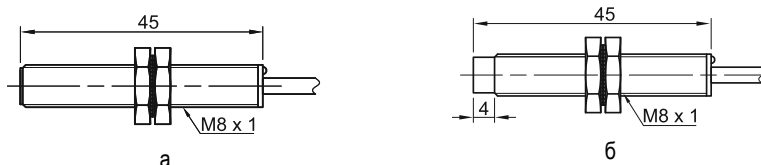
Габаритные и установочные размеры датчиков LA08
